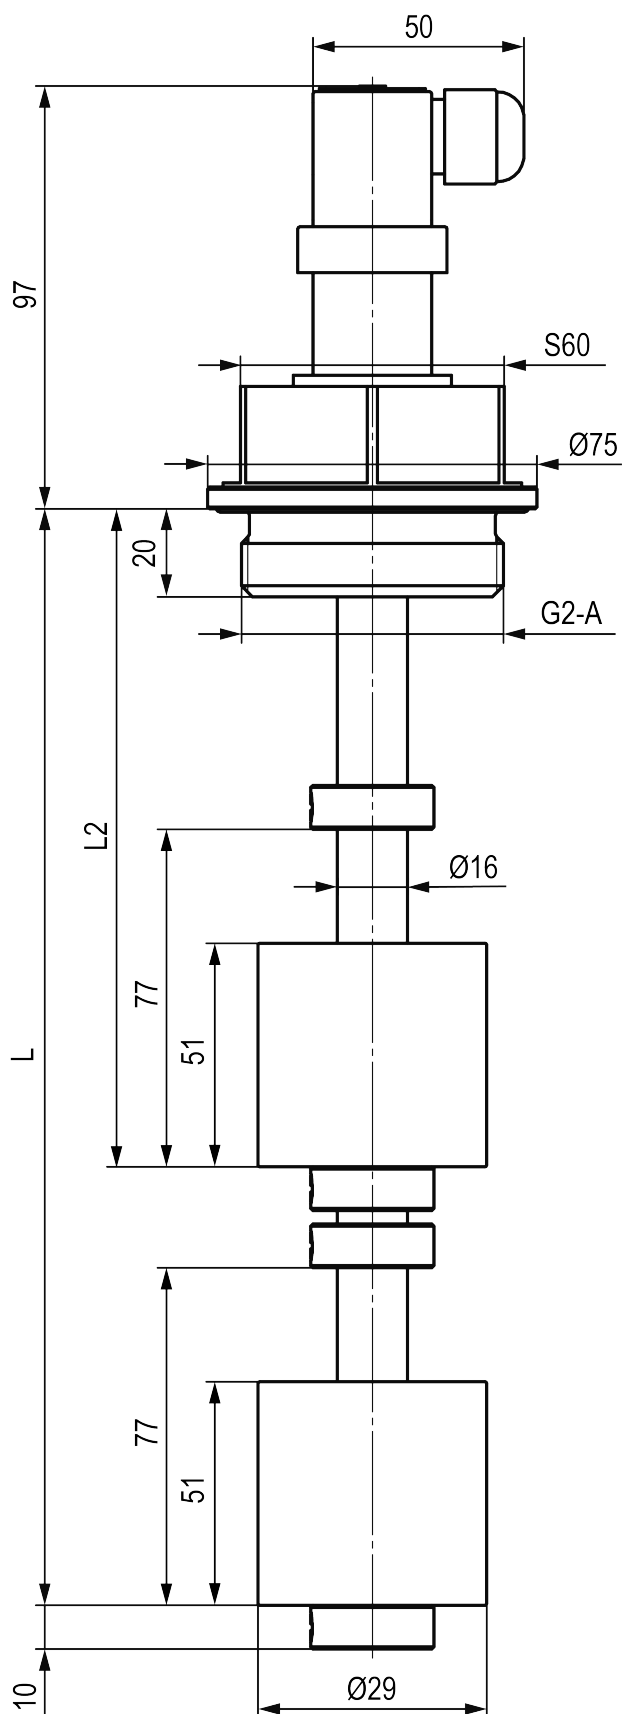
Габаритные и присоединительные размеры одноуровневых ПДУ-П с разъемом DIN 43650 А (наружный монтаж)
